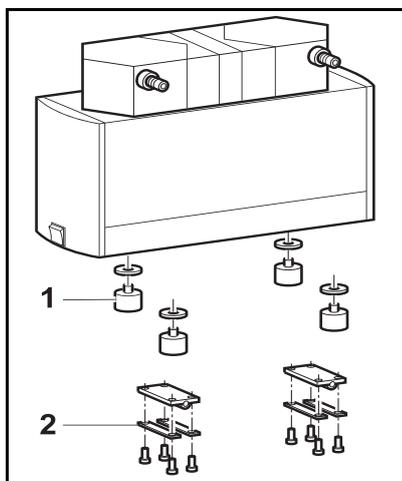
montaggio degli elementi di fissaggio sulla pompa
